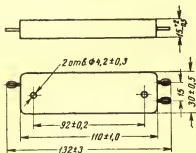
Габаритный чертеж столбов КЦ401А.
